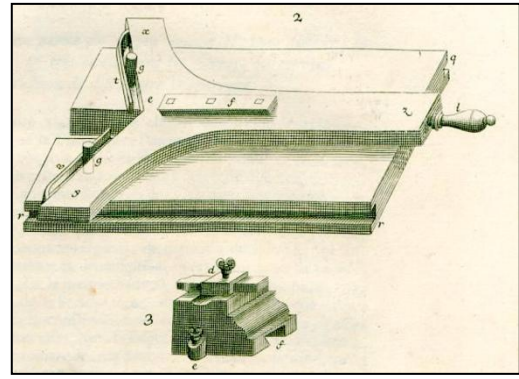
Værktøjssupports dele, Planche 59, detalje (efter Cherubin d'Orléans, 1671) ingen tegnforklaring
